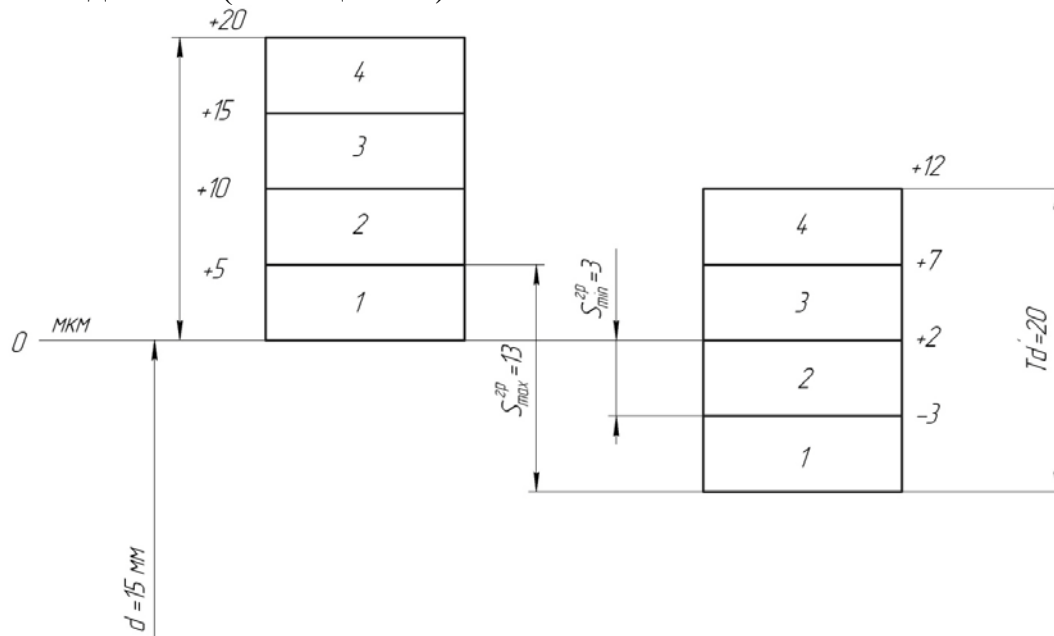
Схема полей допусков соединения «вал—отверстие»
